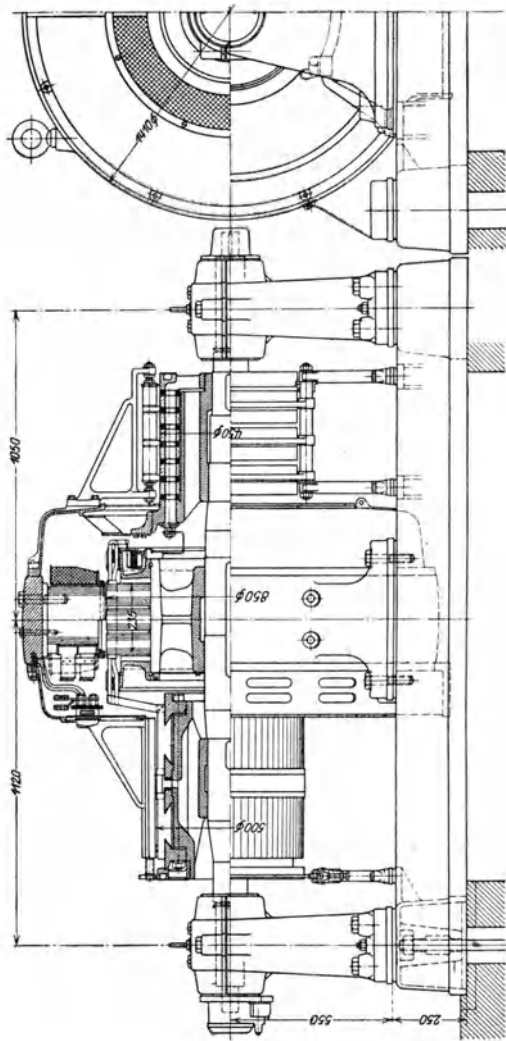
Sechschphasenmotor des Sachsenwerks.
